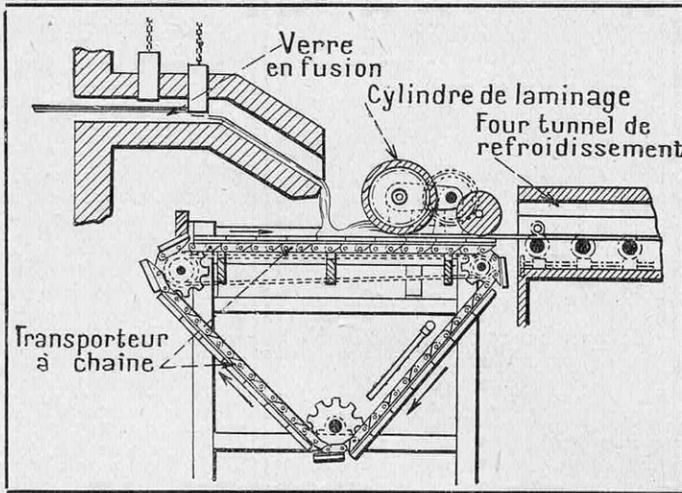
SCHÉMA DE LA FABRICATION DES GLACES PAR LE PROCÉDÉ FORD
